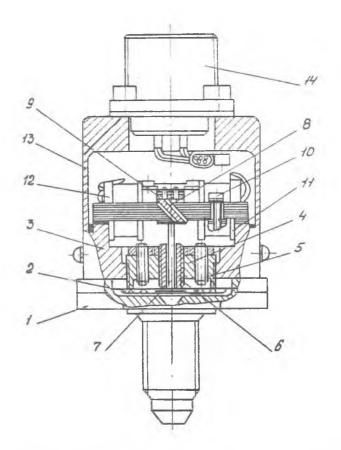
Конструктивная схема цатчика типа ДОЛ: 1 — корпус; 2 — меморана; 3 — кришка; 4 — упор резьбовов; 5 — винти; 6 — втулка; 7 — шток; 8 — якорь; 9 — пружина возвратная; 10 — винти; 11 — катушка верхняя; 12 — катушка нежняя; 13 — кожух; 14 — вилка
